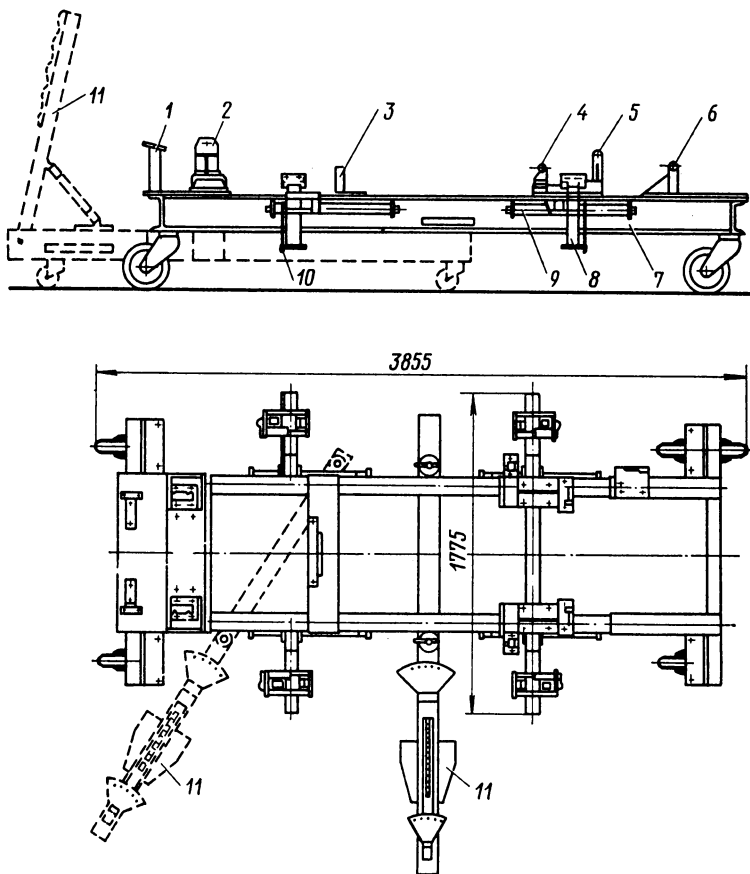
Установка для контроля и правки кузовов БС-123.000
